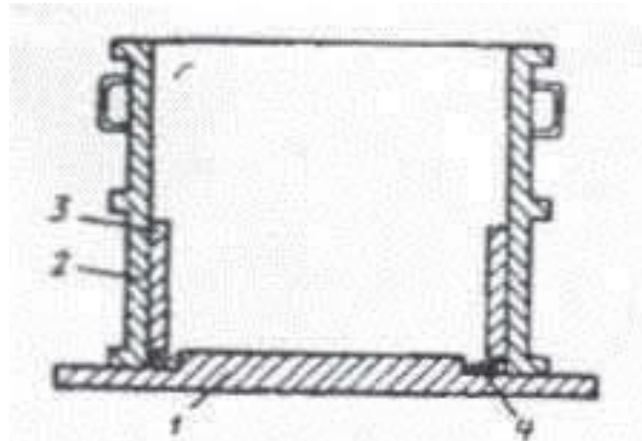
Схема підготовки шихти для плавки феротитану:
